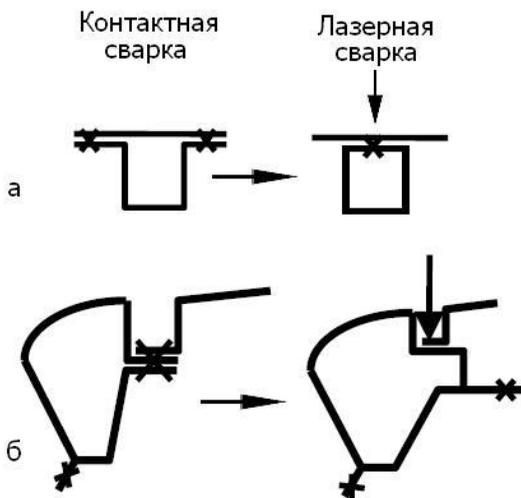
Панель, изготовленная лазерной сваркой с проплавлением наружных листов
